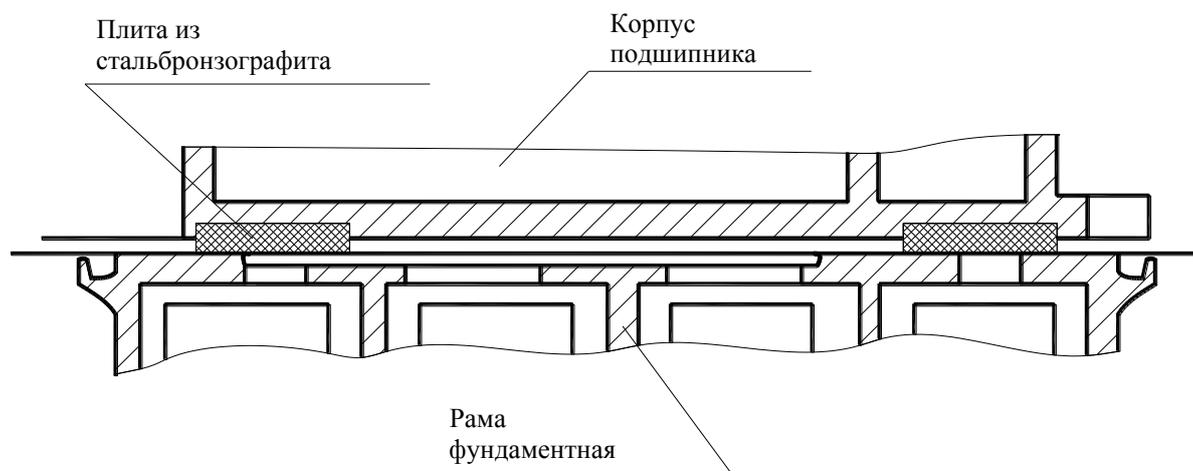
Пример установки на поверхность скольжения корпуса подшипника опорных пластин из стальбронзографита
